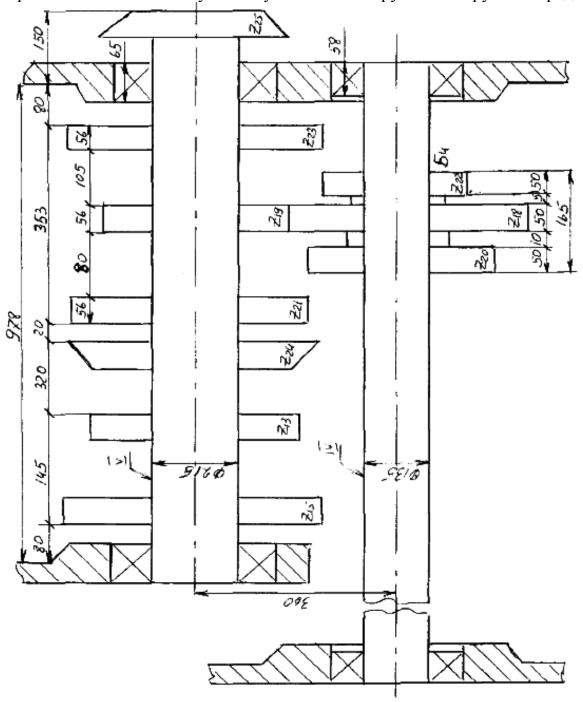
Компоновочная схема развертки наиболее нагруженной группы передач
